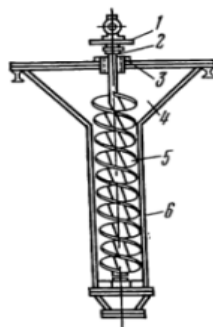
Вертикальный вибросмеситель: 1 – вибропривод; 2 – пружина; 3 – втулка;
